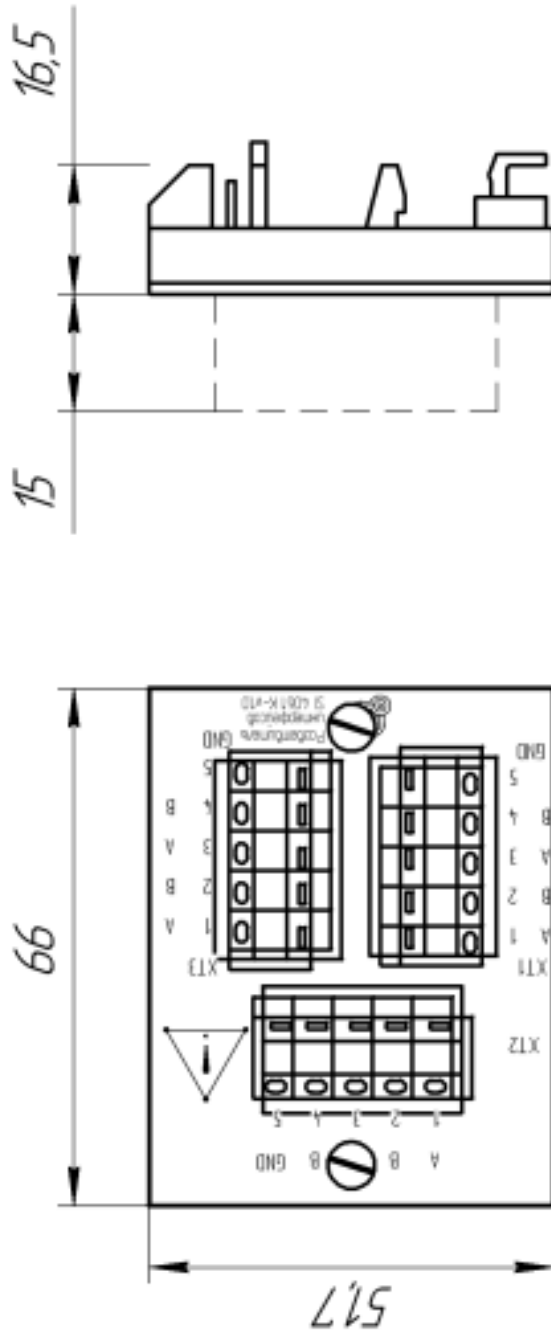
Габаритные и установочные размеры разветвителя SI 4030K, SI 4061K
